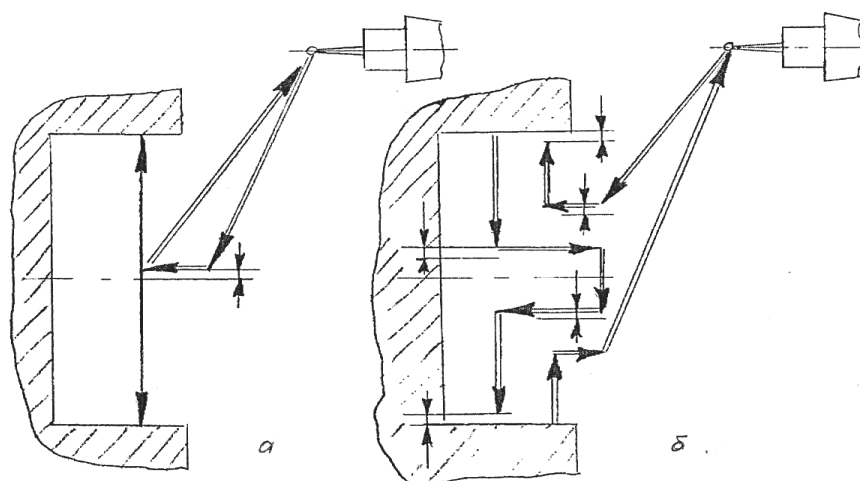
Схемы измерения отверстия обрабатываемой корпусной заготовки
